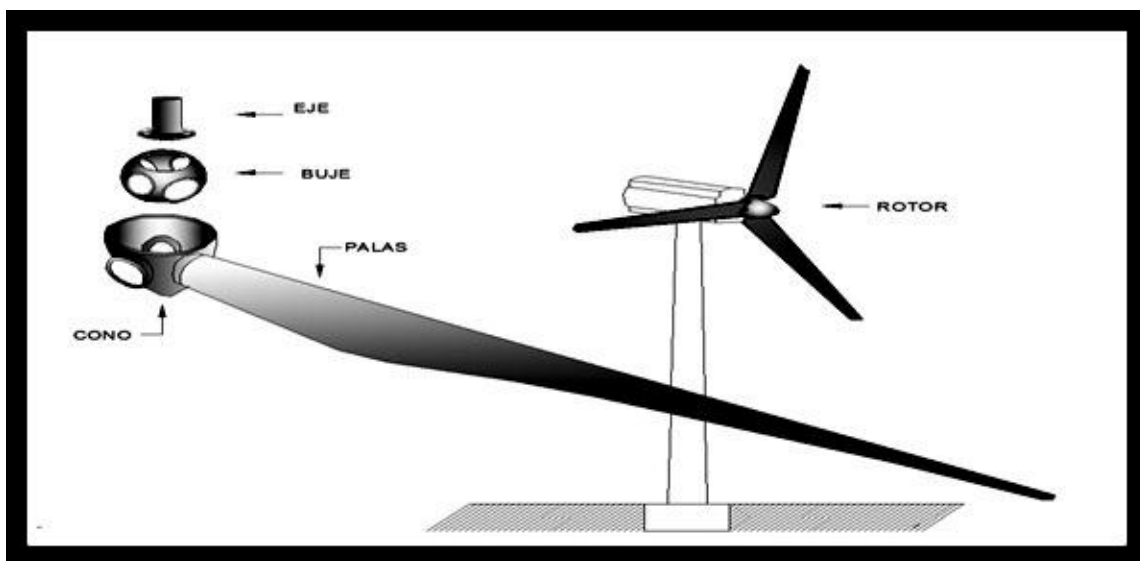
Partes que conforman el rotor de una turbina eólica.
